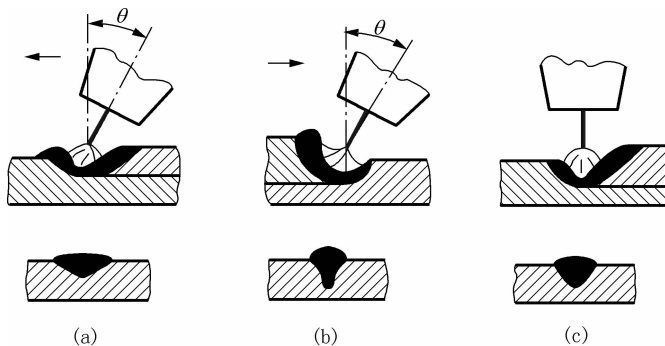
左焊法和右焊法对焊缝成型的影响
